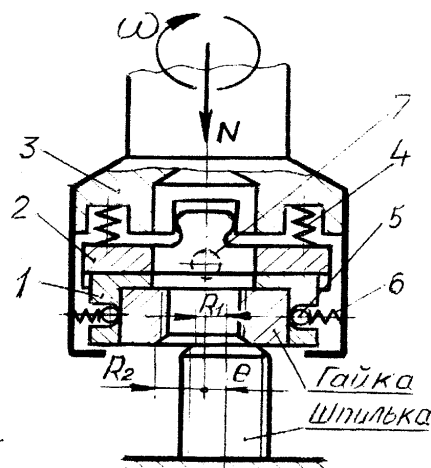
Схема податливого базування гайки: 1 - база гайки; 2 - база гайки; 3 - шпindelь; 4 - осьові пружини; 5 - кульки; 6, 7 - радіальні пружини;  $R_1$  - радіус фаски шпильки;  $R_2$  - радіус фаски гайки;  $N$  - осьове зусилля шпindelя;
